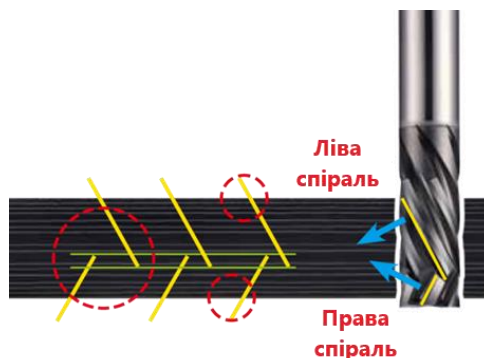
Схема роботи кінцевої фрези CDR KORLOY [23]
